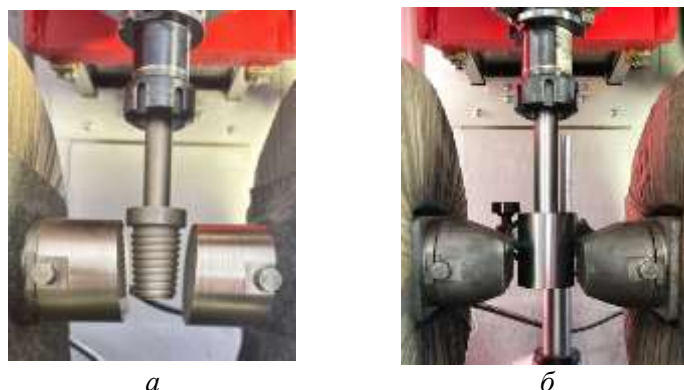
Установленные в устройство для МАП образцы: а – с наружной резьбой; б – с внутренней резьбой
